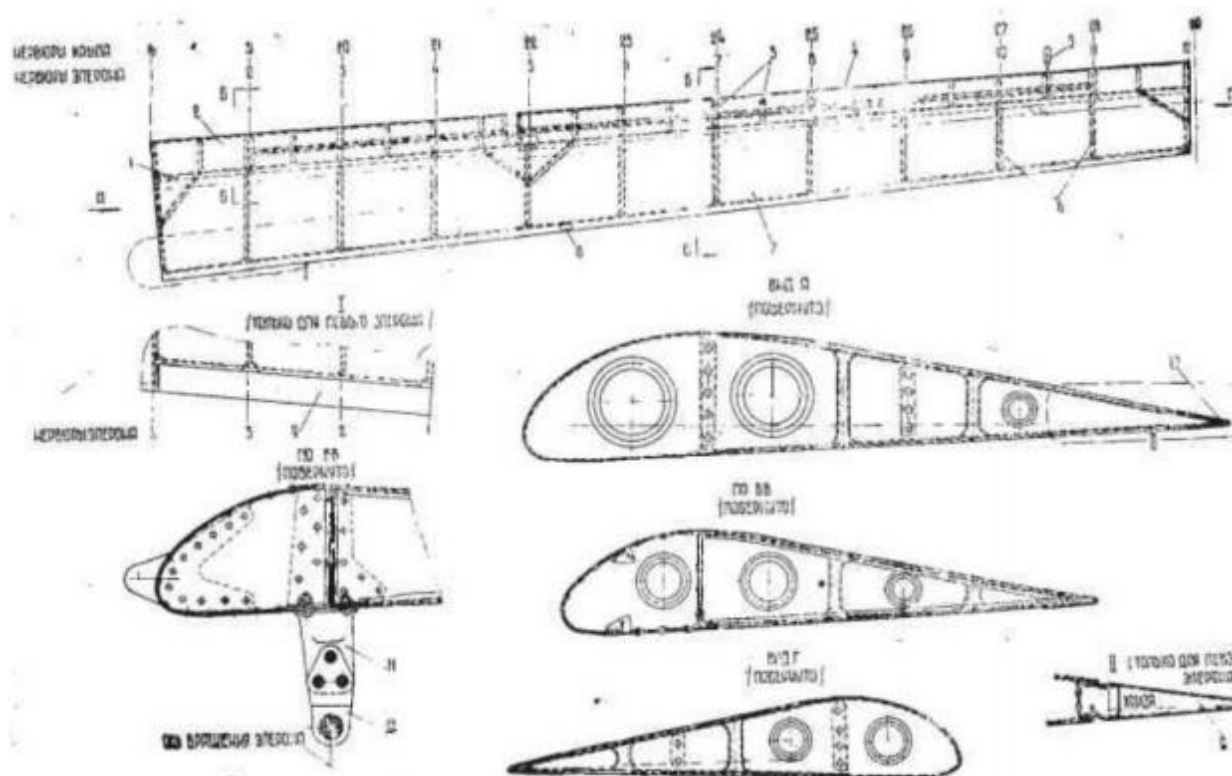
Правий елерон: 1-лонжерон; 2-обшивка із Д16АТП; 2-носки нервюр; 4-стрингер; 5-балансер елерона; 6- нервюри; 7-обшивка з тканини АМ-100; 8-законцовка; 9-тример; 10-вкладиш із пенопласту ЛХВ-1; 11-кронштейн підвіски елерона; 12-вилка.
